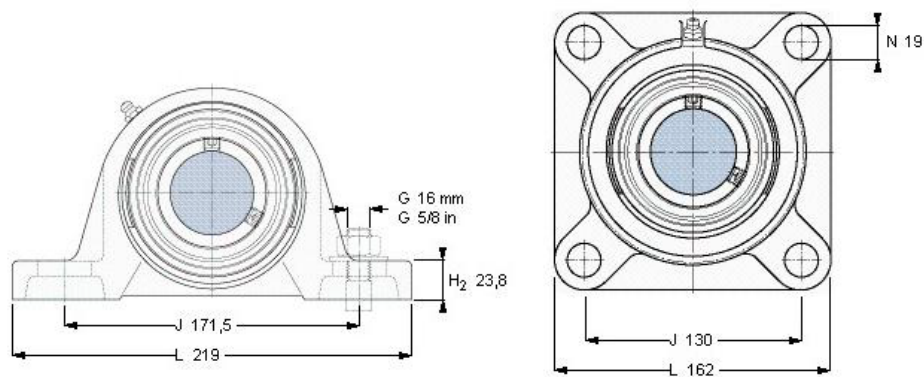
Dimensiones generales del los rodamientos seleccionados.
